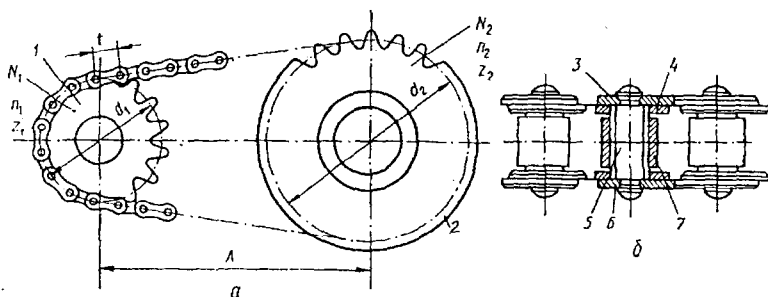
Цепная передача: а – общий вид; б – конструкция втулочно-роликной цепи; 1 – ведущая звездочка; 2 – ведомая звездочка; 3 – наружное звено; 4 – внутреннее звено; 5 – ось; 6 – втулка; 7 – ролик
